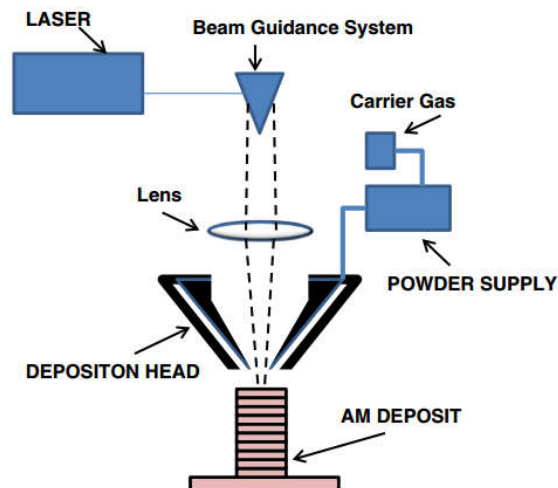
Prinzip Pulverauftragsschweißen [14]
